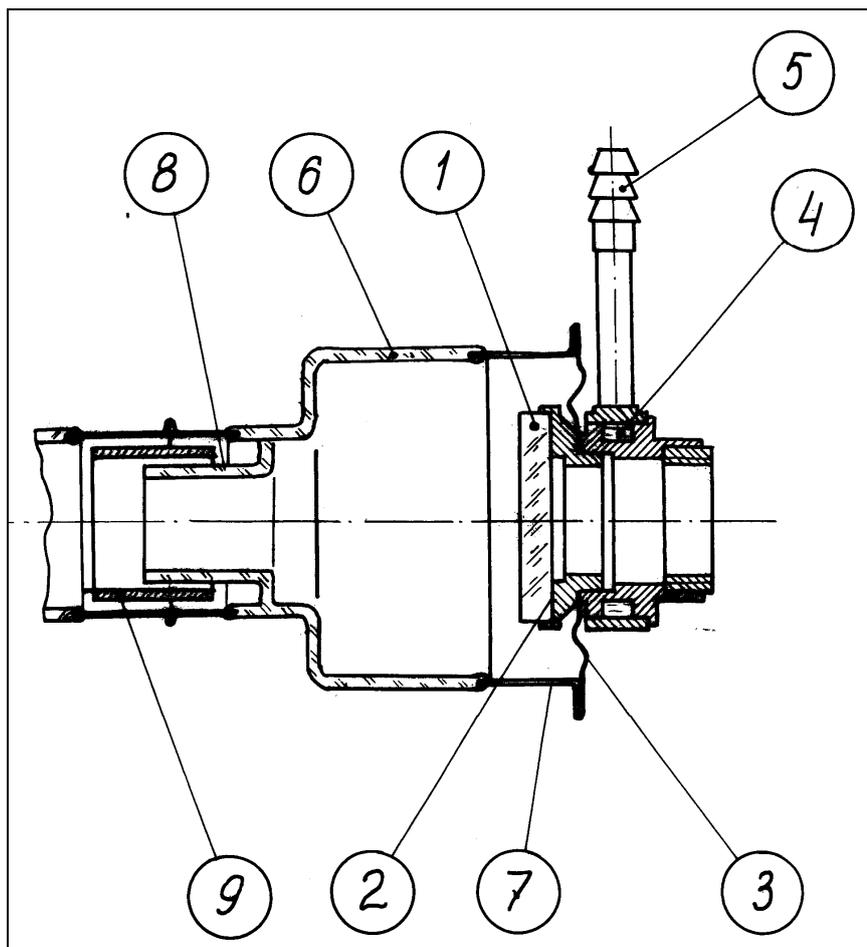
Схема узла выходного зеркала излучателя лазера ЛГ-74: 1 – полупрозрачное зеркало, 2 – цилиндрический стакан, 3 – коваровая манжета, 4 – водяное охлаждение, 5 – штуцера для подачи воды, 6,7 – концевик с коваровым кольцом, 8 – защитный цилиндр, 9 – электрод.
